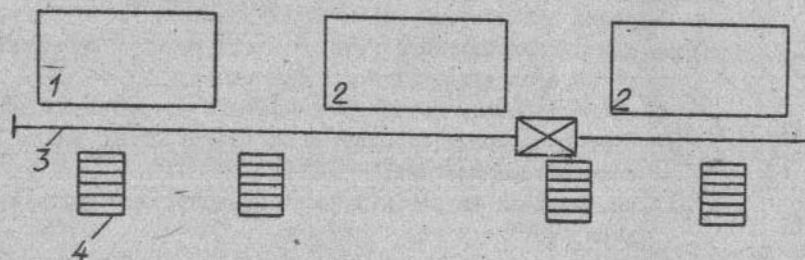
Робототехнический комплекс для обработки деталей типа тел вращения: 1 - фрезерно-центровальный станок; 2 - токарные станки, 3 - порталный робот, 4 - пристаночные локальные накопители
